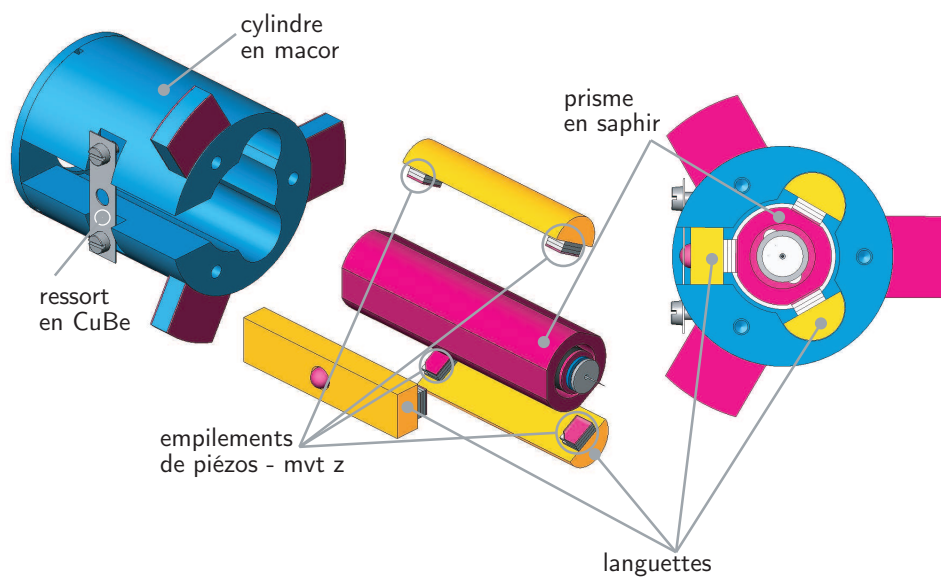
Vue éclatée et de face de la tête du STM.
